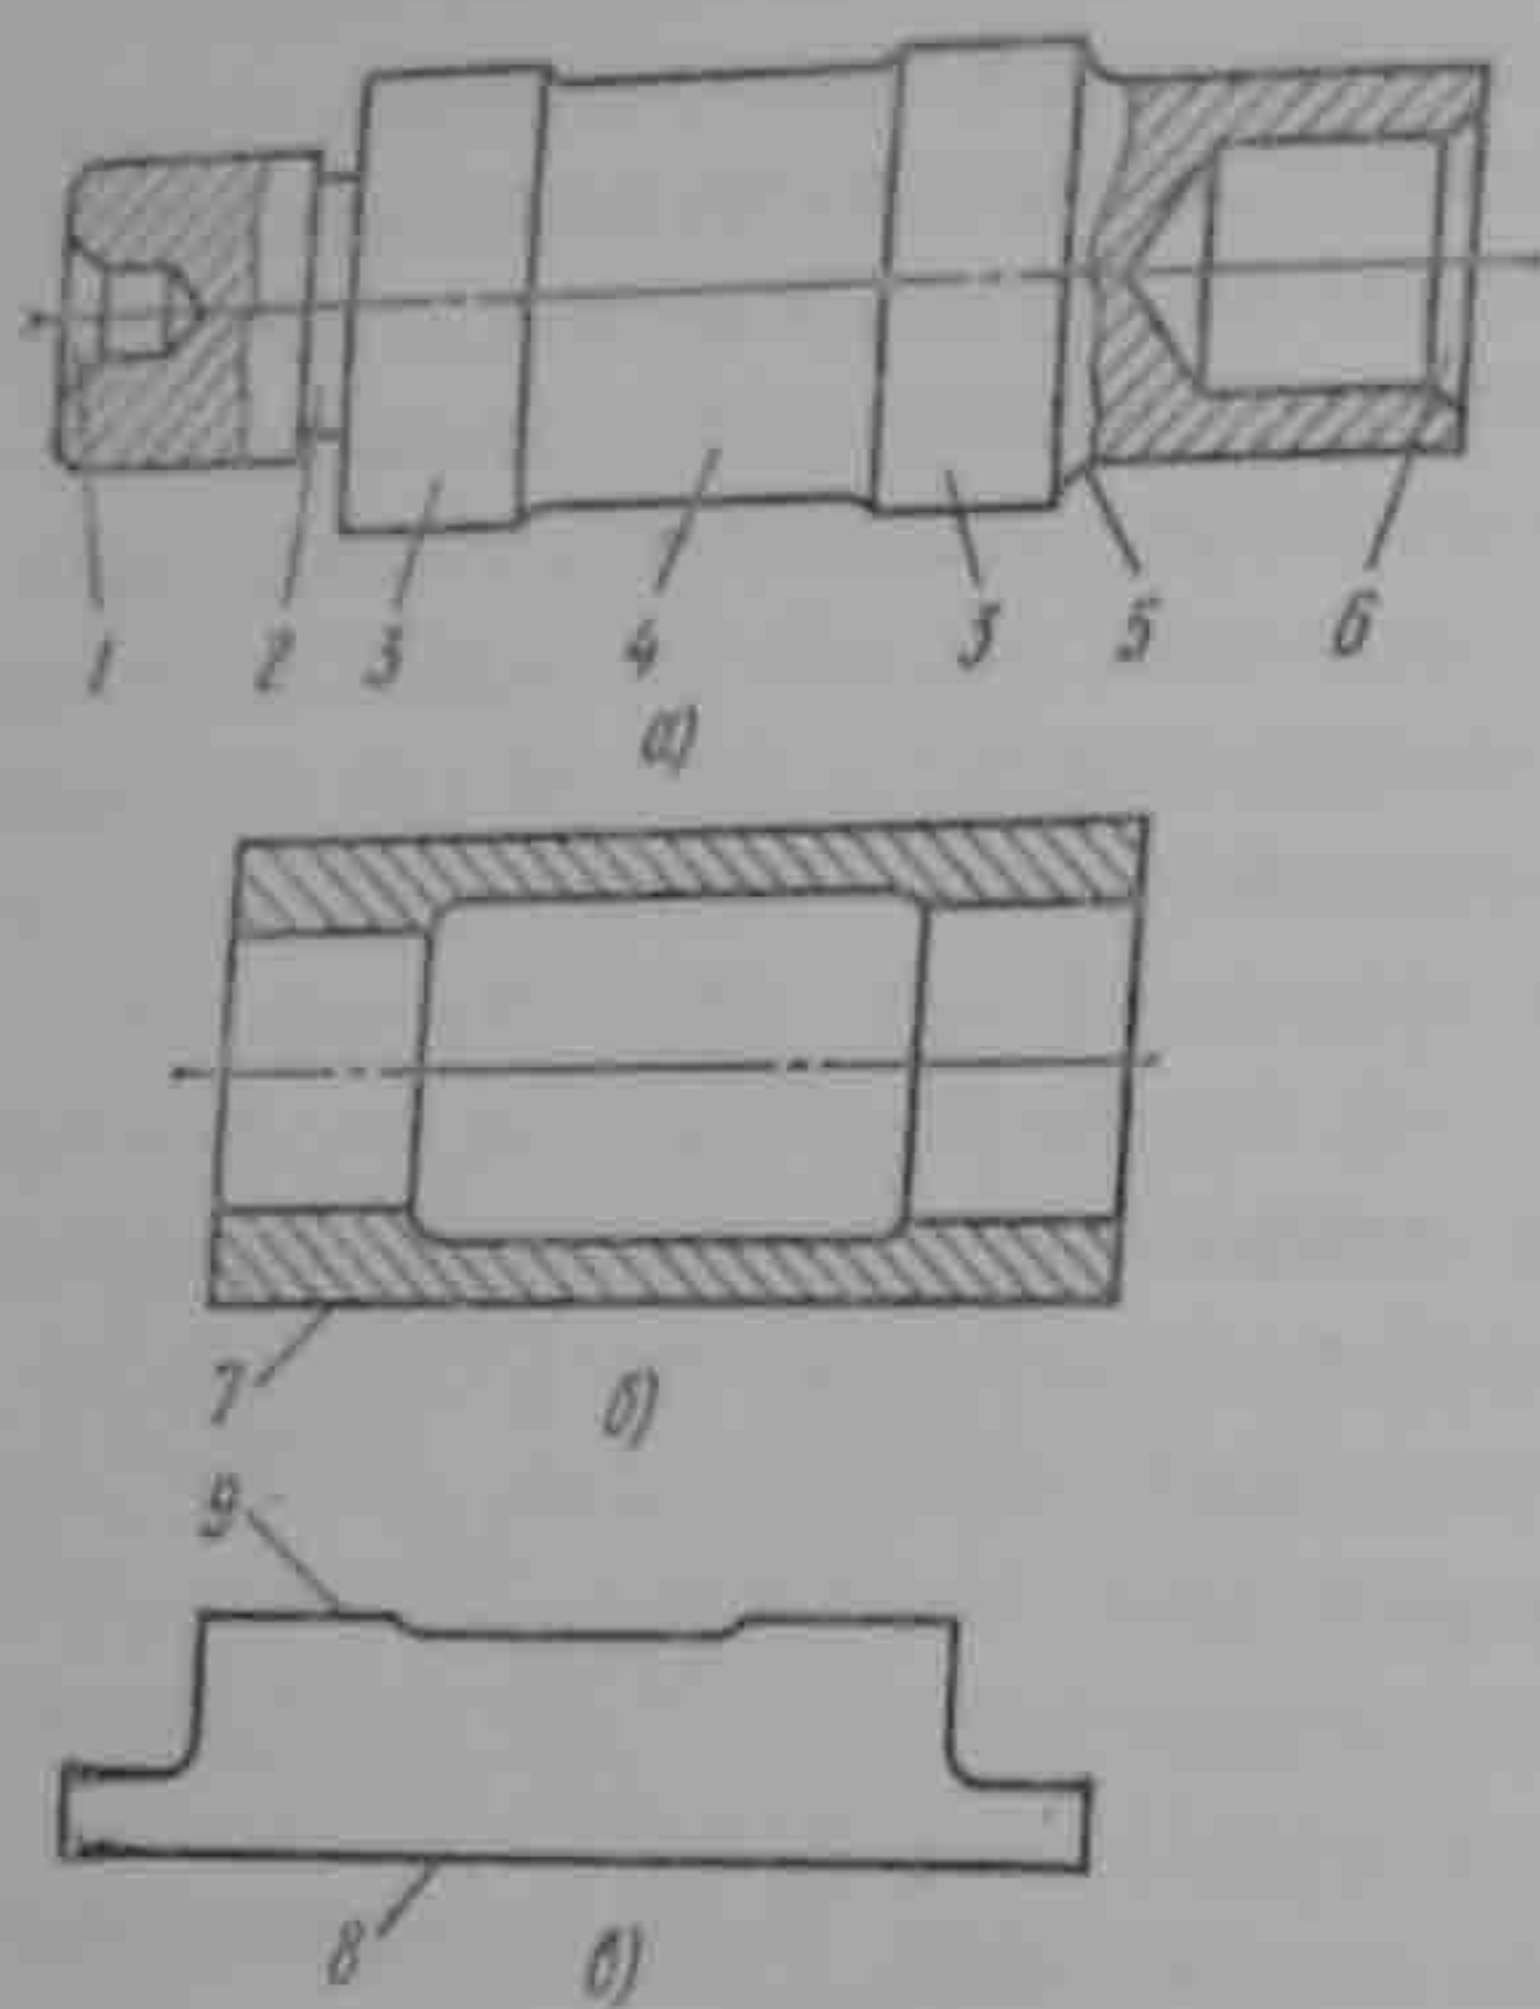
Форма деталей, обрабатываемых на станках шлифовальной группы
